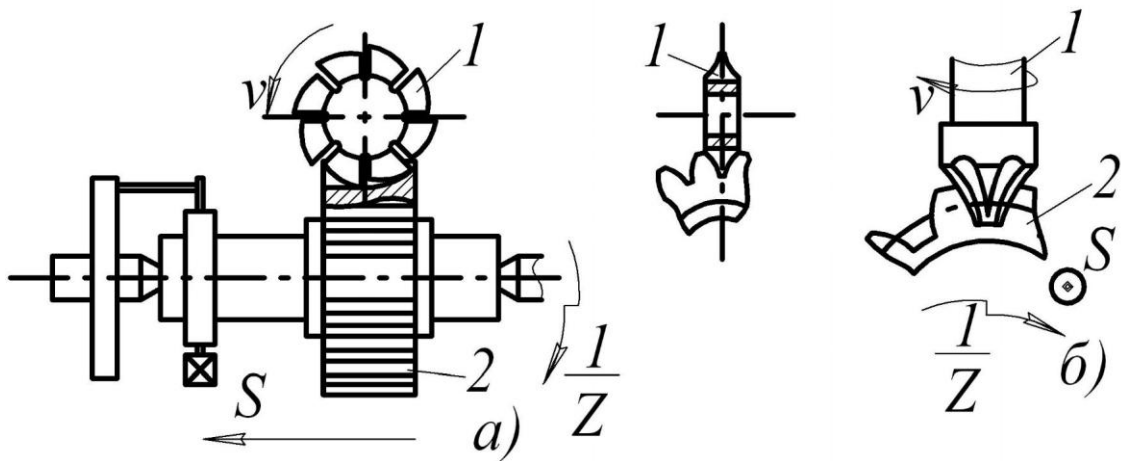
Схеми фрезерування зубів за методом копіювання 1 - фреза; 2 - оброблюване колесо
